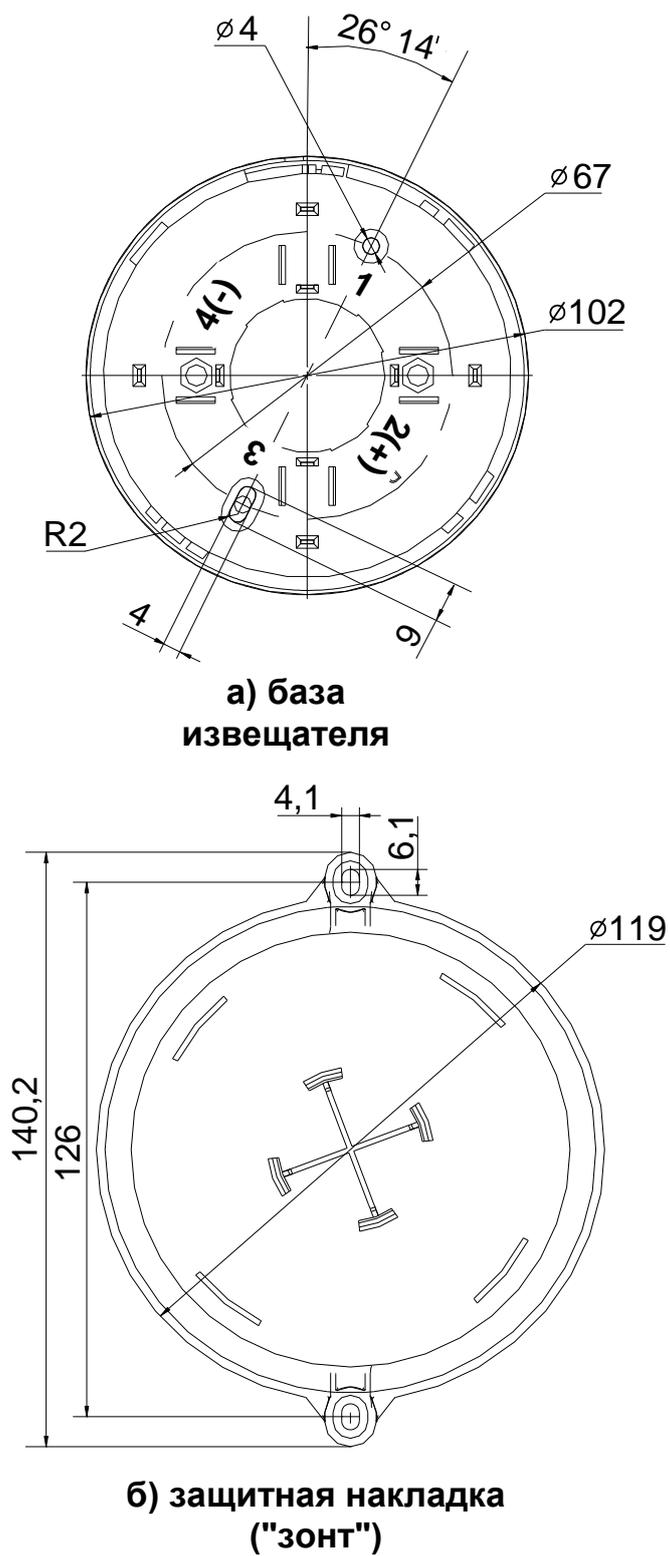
А2ДПИ. Габаритные и присоединительные размеры базы и защитной накладки "Зонт".
